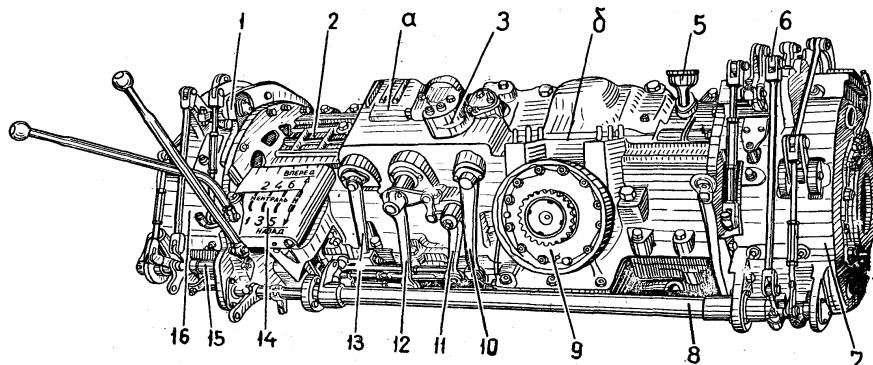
Коробка передач із кулісою і механізмами керування поворотом:
